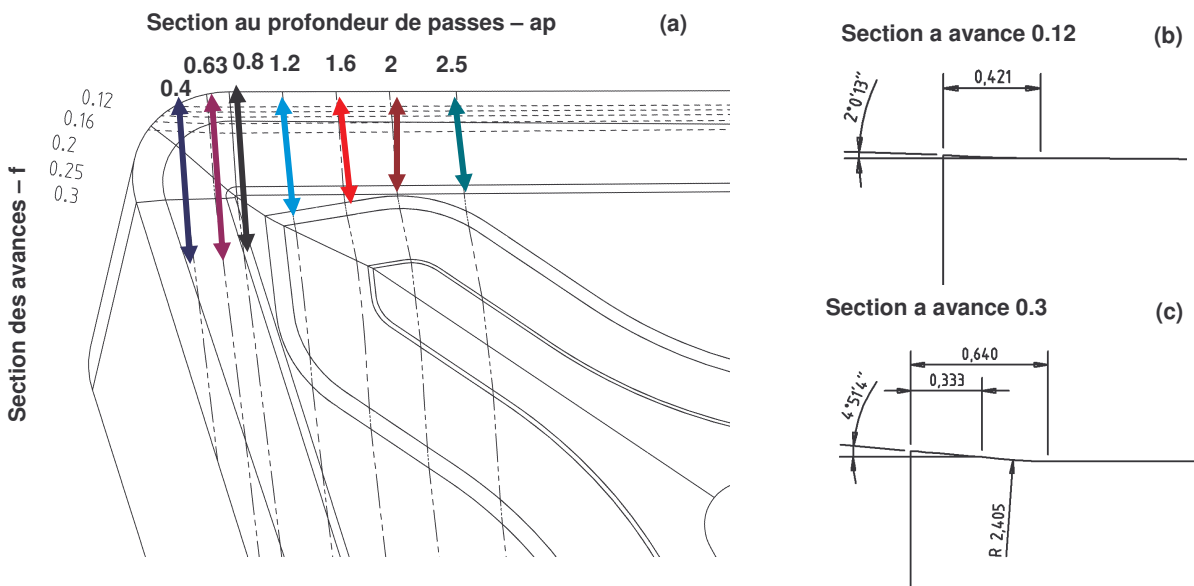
(a) Plan de la plaquette CNMG120408 M5 avec les sections a_p et f , (b) section de la plaquette pour une avance 0.12, (c) section de la plaquette pour une avance 0.3.
